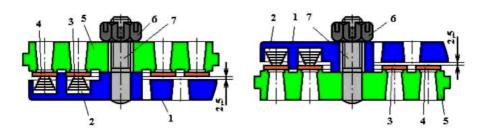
Всасывающий (а) и нагнетательный (б) клапаны компрессора КТ-6 1- седла, 2- большие клапанные пластины, 3- малые клапанные пластины, 4- конические ленточные пружины, 5- обоймы (упоры), 6- корончатые гайки, 7- шпильки
